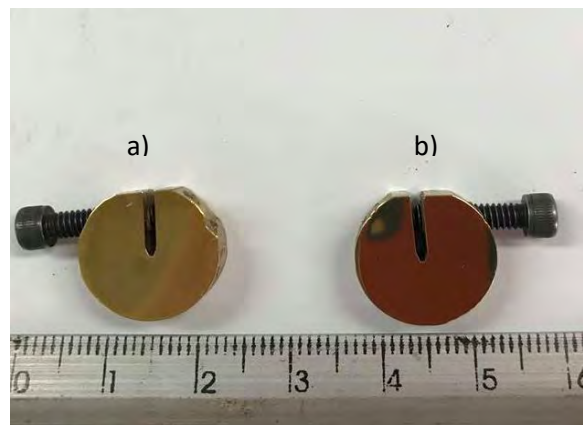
Probetas sometidas a fuerzas de torque. a) Probeta de acero y b) Probeta de cobre.
